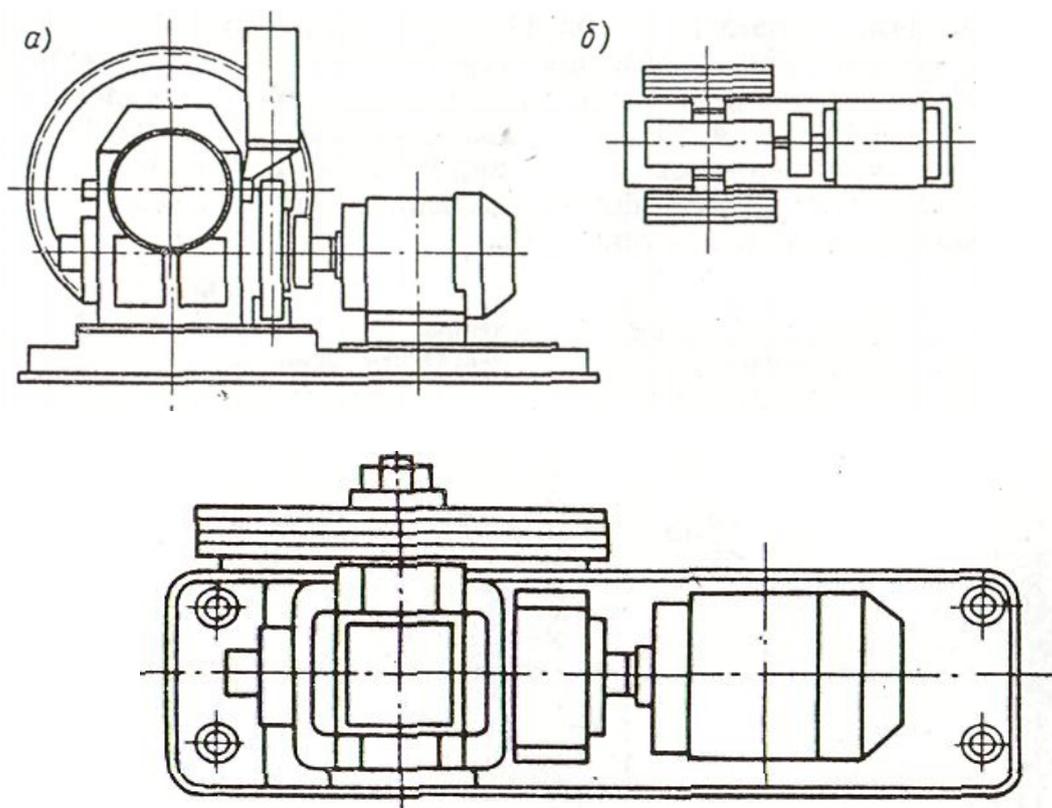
Лифтовые редукторные лебедки с глобоидными передачами
